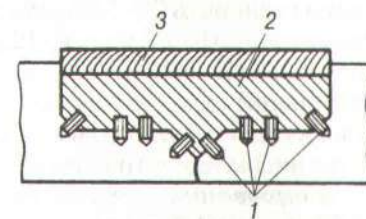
Підготовка чавунного виробу до холодного зварювання з сталевими шпильками:
